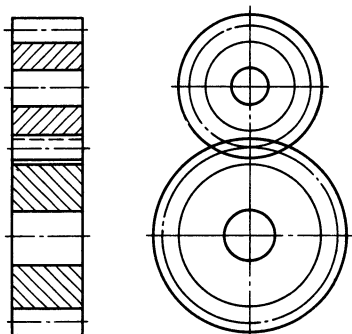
Условное изображение зацепления цилиндрическими зубчатыми колесами
